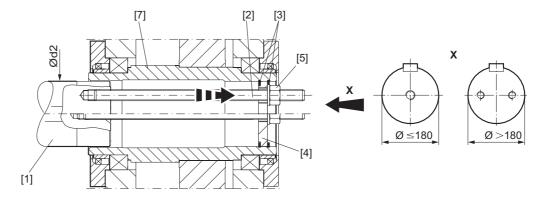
Montaje de reductores horizontales con unión por chaveta
